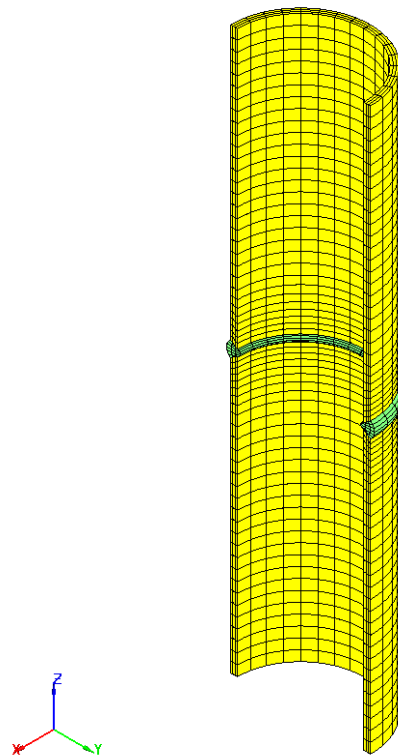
Косой стык со сварным швом. ИПКЭ
